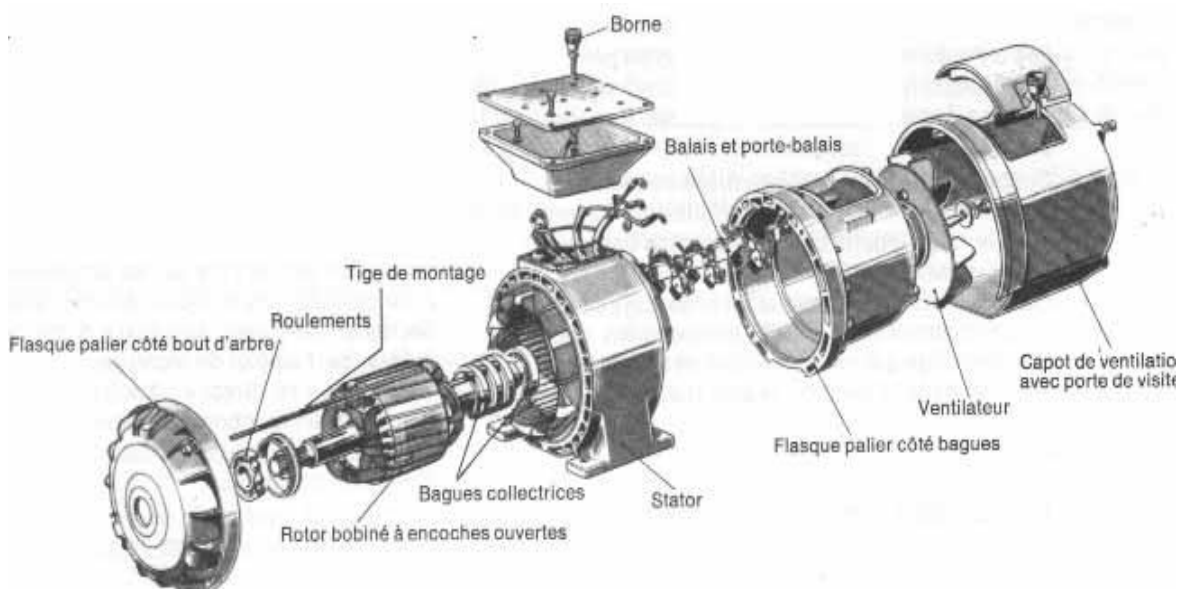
Vue éclatée d'un moteur asynchrone à rotor bobiné
